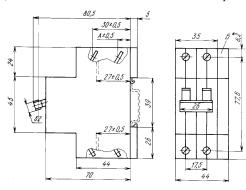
Габаритные, установочные, присоединительные размеры выключателей однополюсных типа ВА23-29.
